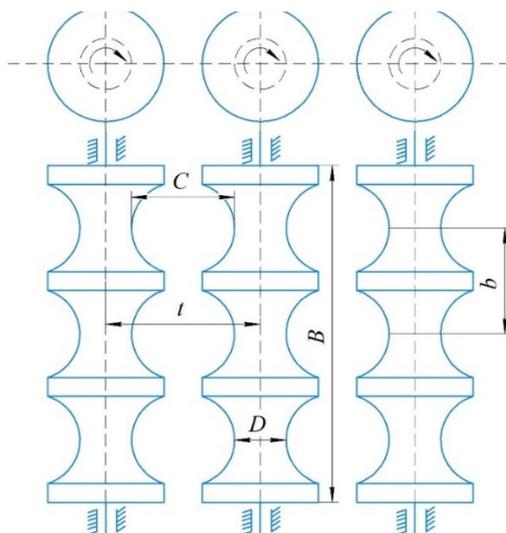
Вальцы: В – ширина рабочей поверхности; D – диаметр роликов по впадинам; t – шаг роликов; b – шаг проточек; C – максимальный зазор между смежными вальцами
